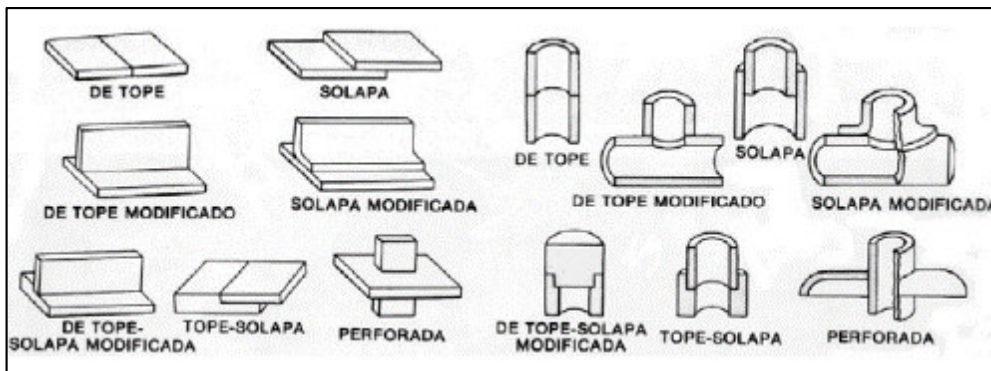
Tipos de juntas para soldadura indirecta para elementos planos y tubulares. (Fuente: [17])
